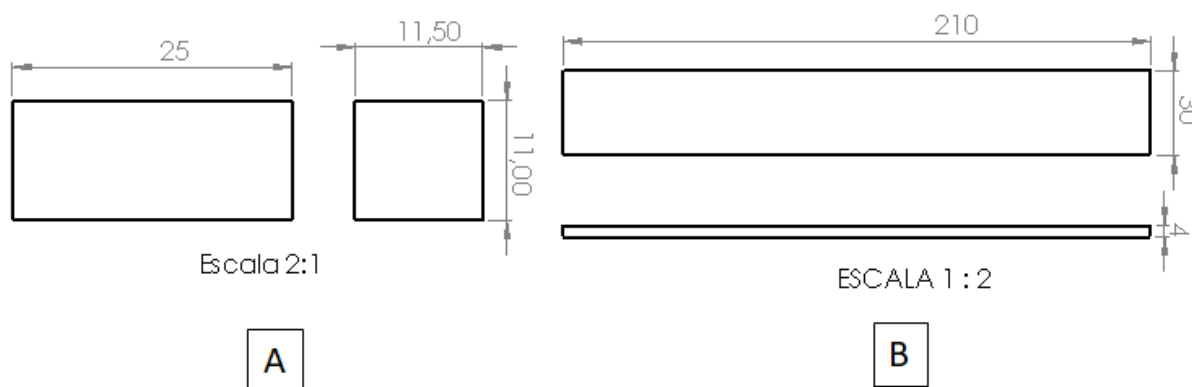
8 Desenho dos corpos de prova a) Tração; b) Compressão.
